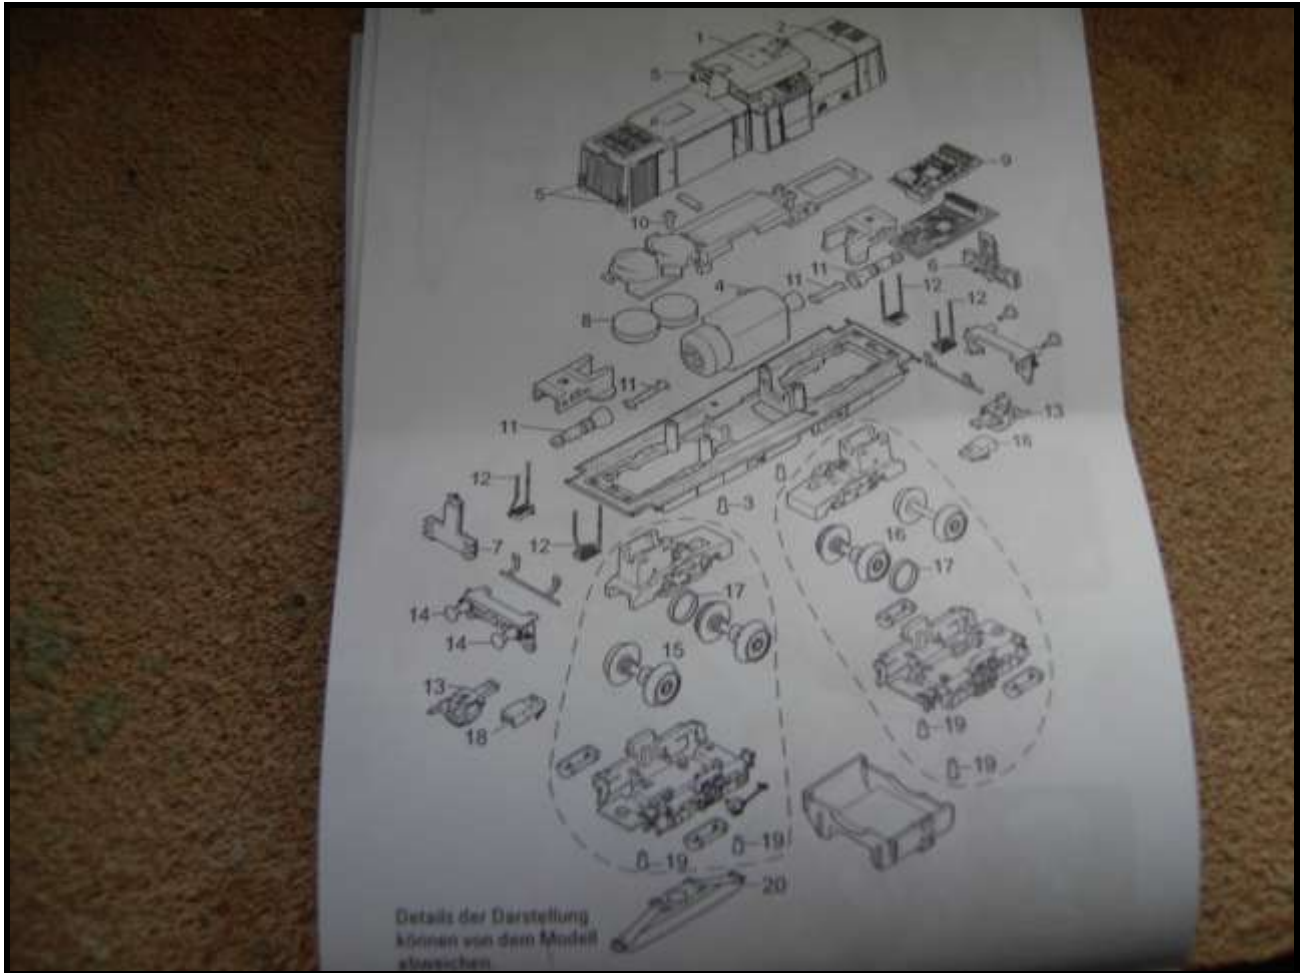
l'esploso della nuova 212 105-1 nel libretto delle istruzioni.
